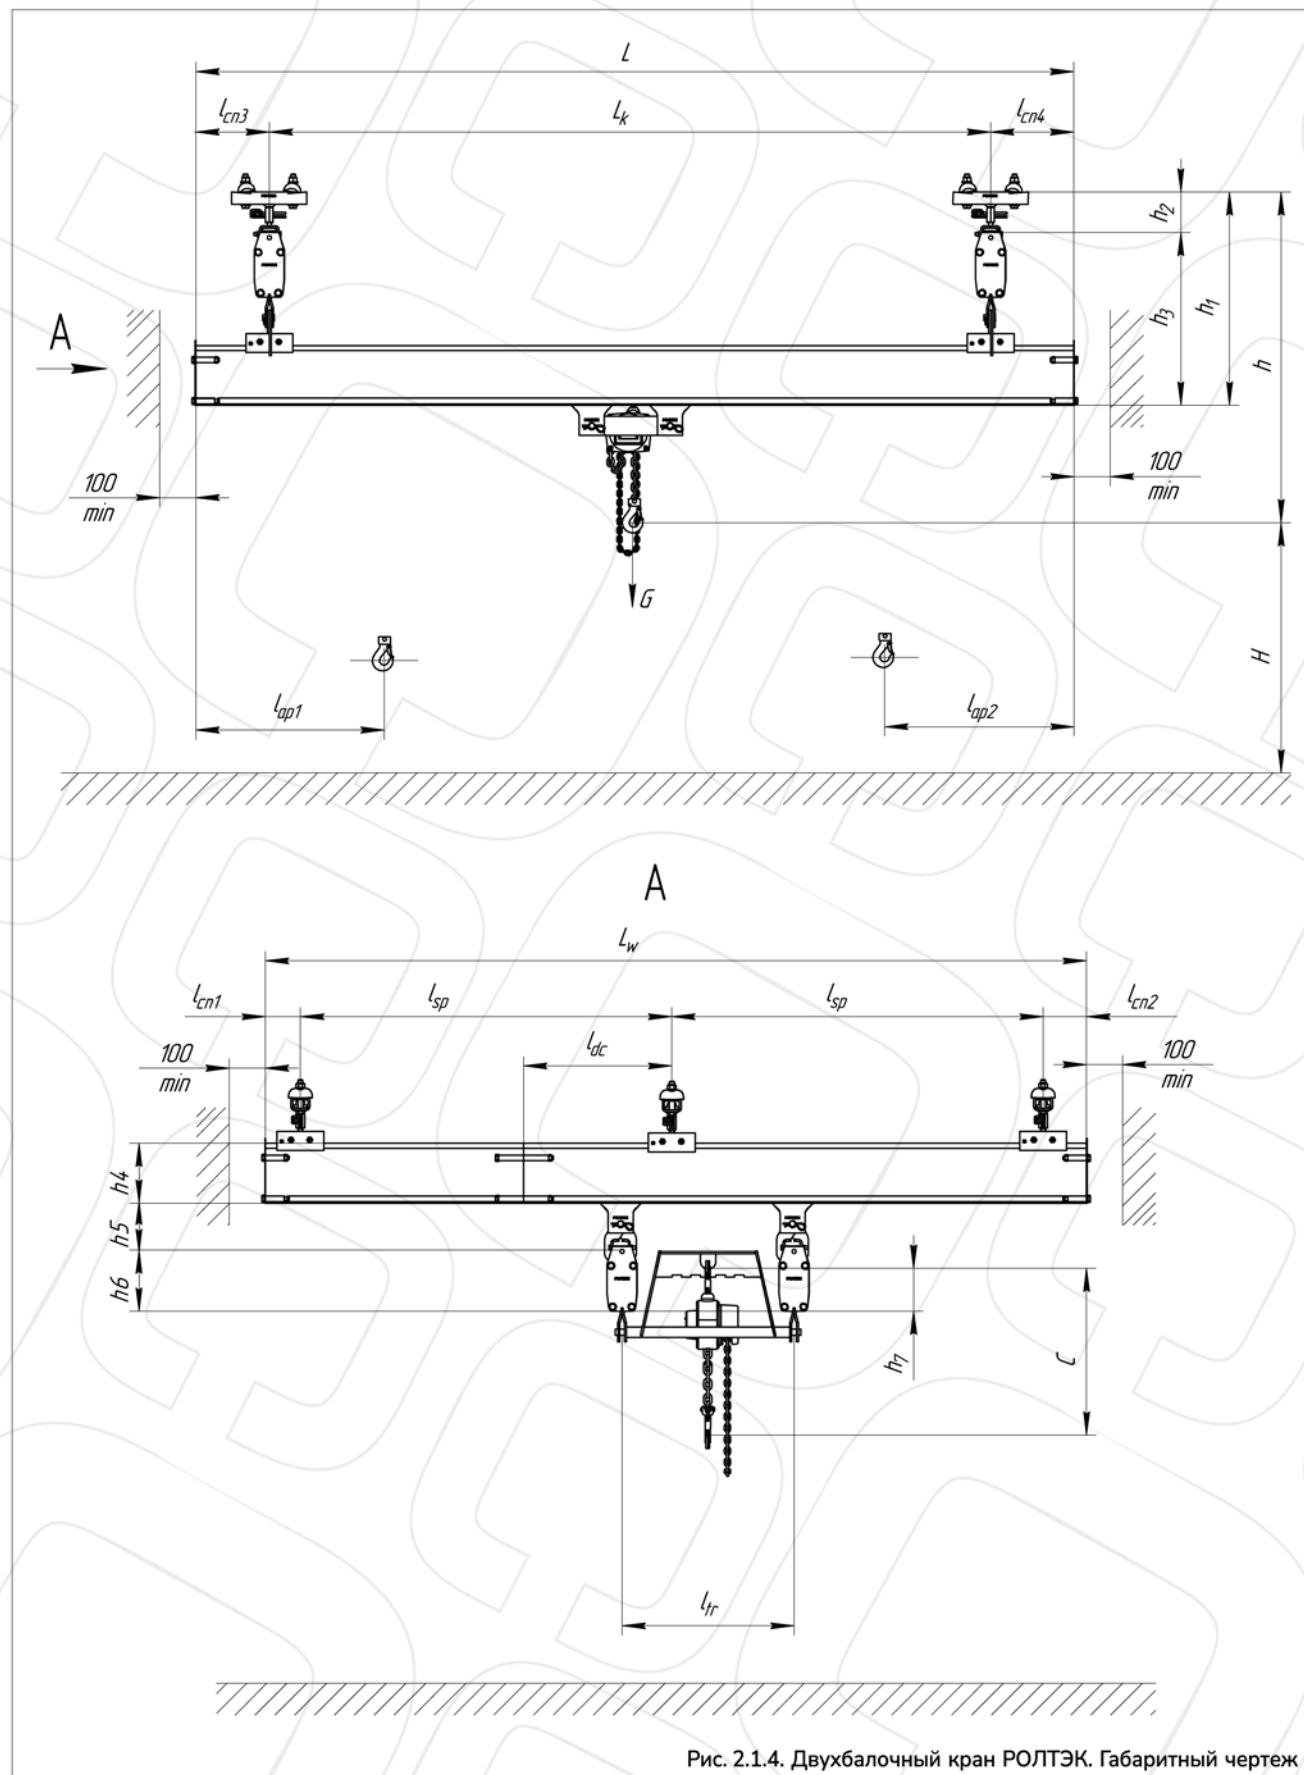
Двухбалочный кран РОЛТЭК. Габаритный чертеж
